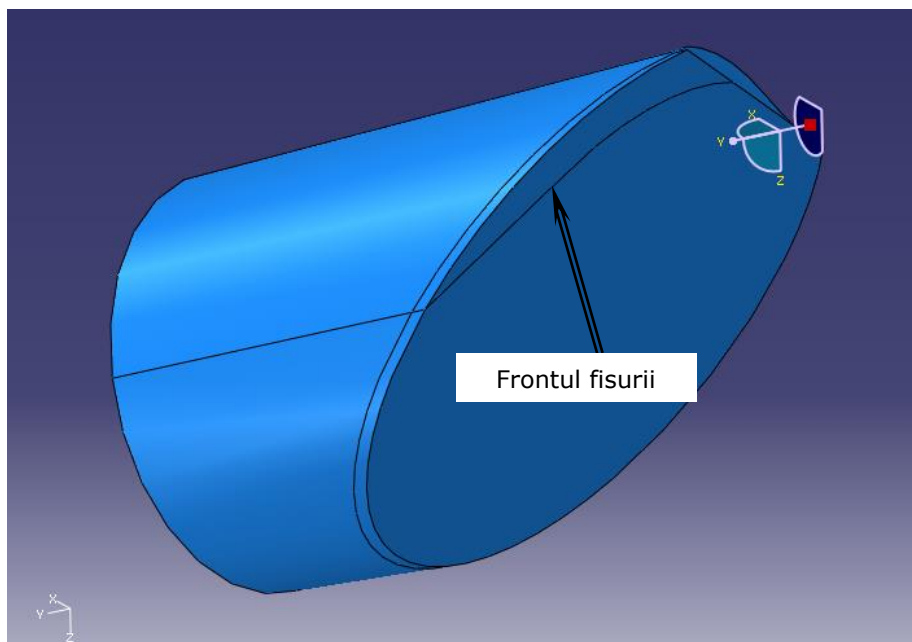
Secțiune în planul fisurii cu lungime fixă (11 mm) și adâncime de 0,7 mm
